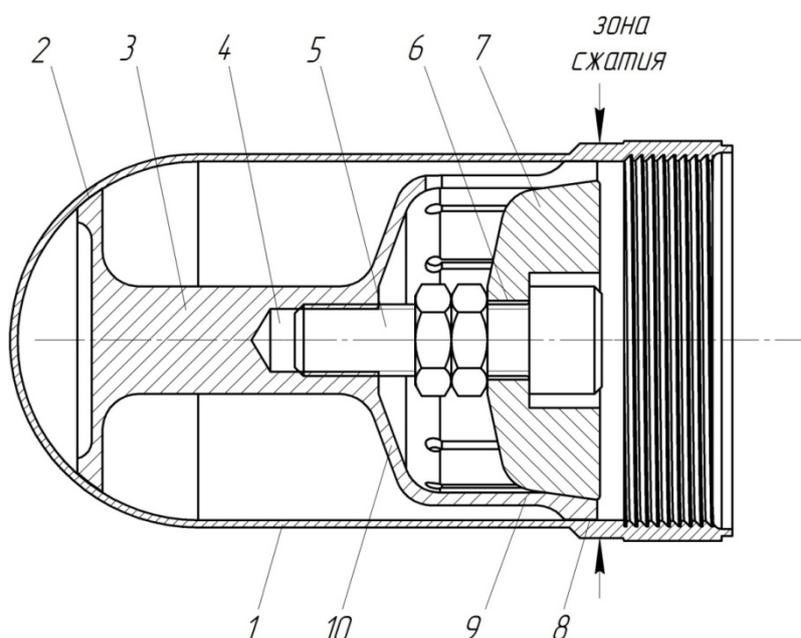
Схема установки разжимной цанги в полости сварного корпуса
